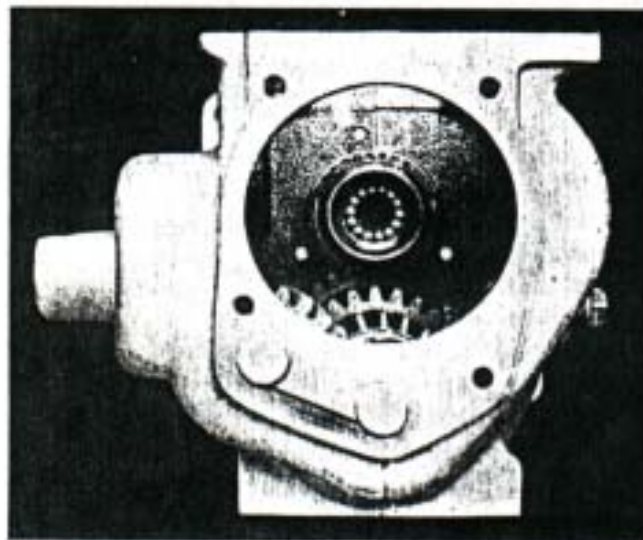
Detalle del cojinete guía, previo al montaje del eje principal.
